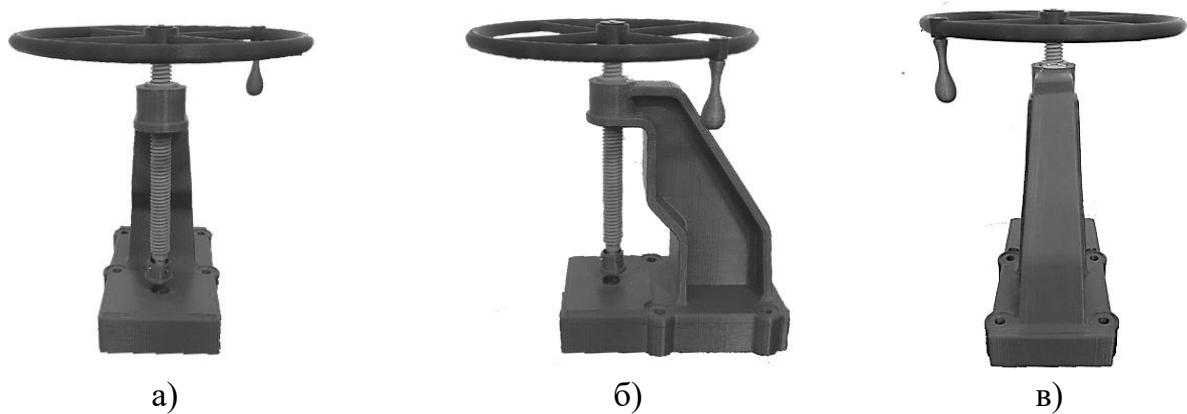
Ручной пресс распечатанный на 3D принтере: а) сборка вид справа б) сборка вид спереди в) сборка вид слева
